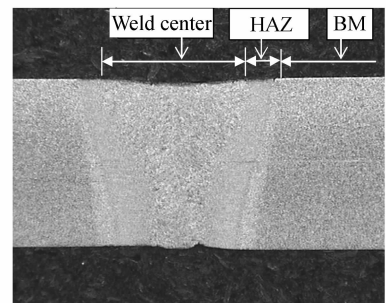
B450LAD 激光焊焊接接头横截面典型宏观金相图
